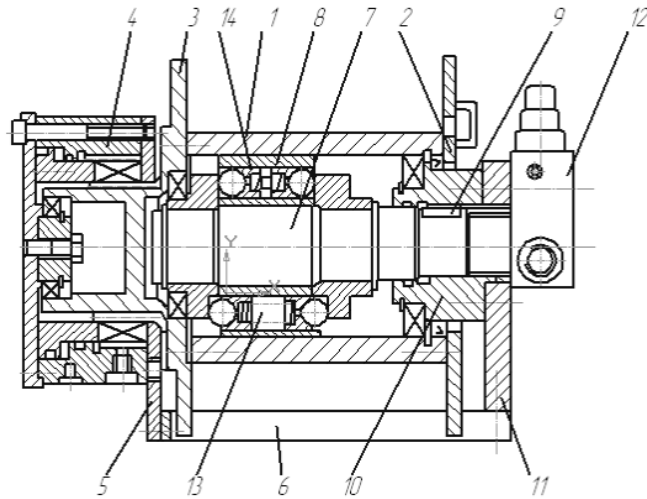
Конструктивна схема мотор-барабана фірми "Rexroth"
